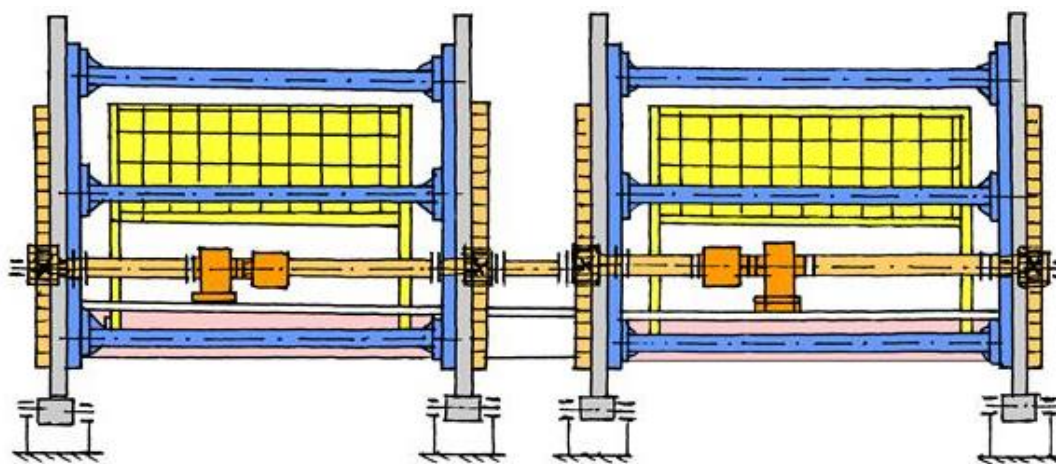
Вагоноопрокидыватель роторного типа в поперечном разрезе
